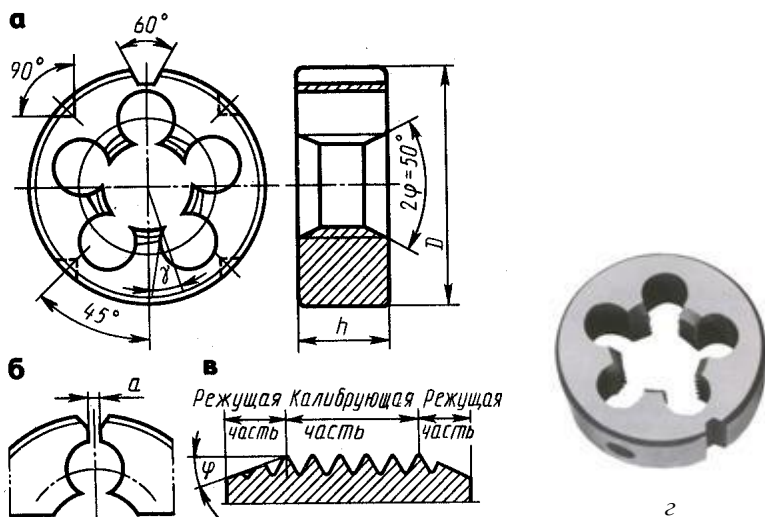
Плашки: а, с – круглая плашка до разрезания; б – разрезанная круглая плашка; в – профиль резьбы рабочей части
